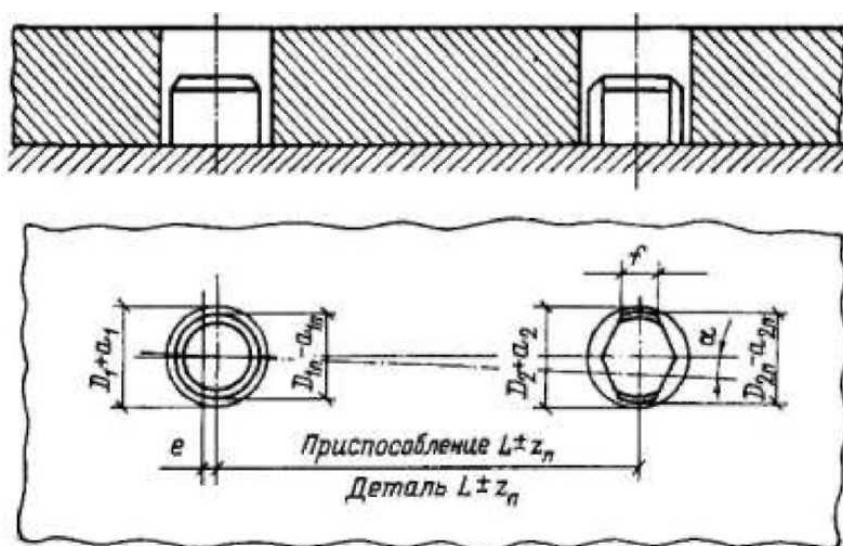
Базирование детали на цилиндрический и срезанный палец
